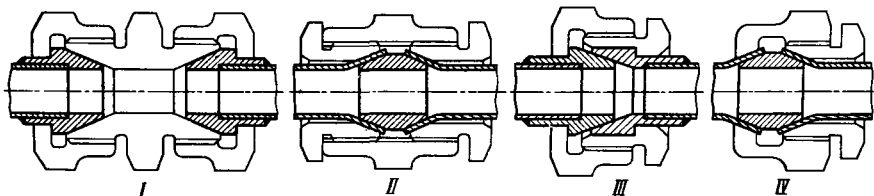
Соединения трубопроводов напрямую с помощью ниппелей
